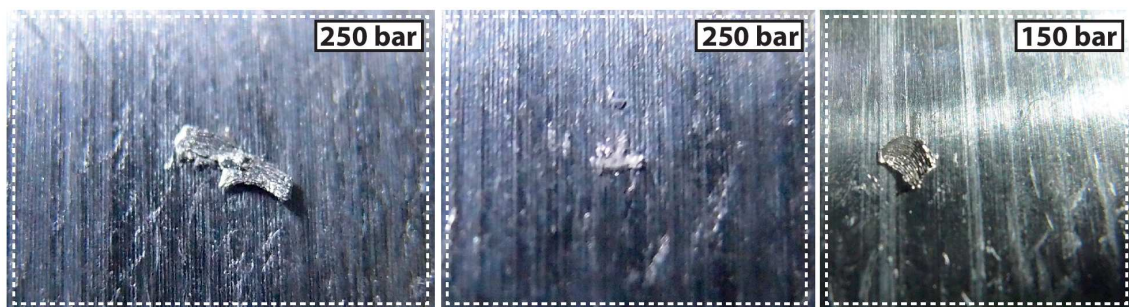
Rayures et fragments soudés sur la surface de la pièce après un usinage à 150 bar et à 250 bar
